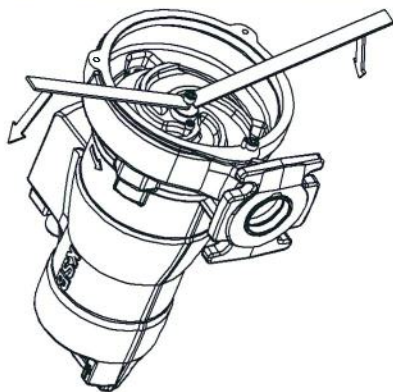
Ramener le sous-ensemble rotor vers le fond d'aspiration
